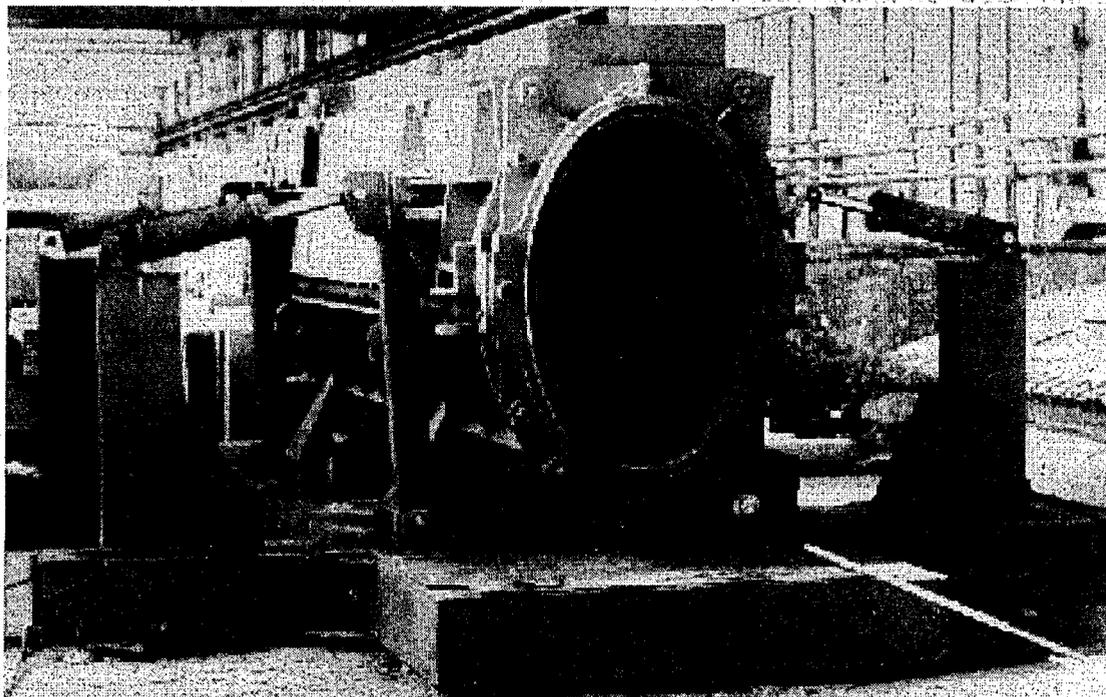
Металлоформа для изготовления оvoidальных железобетонных труб
